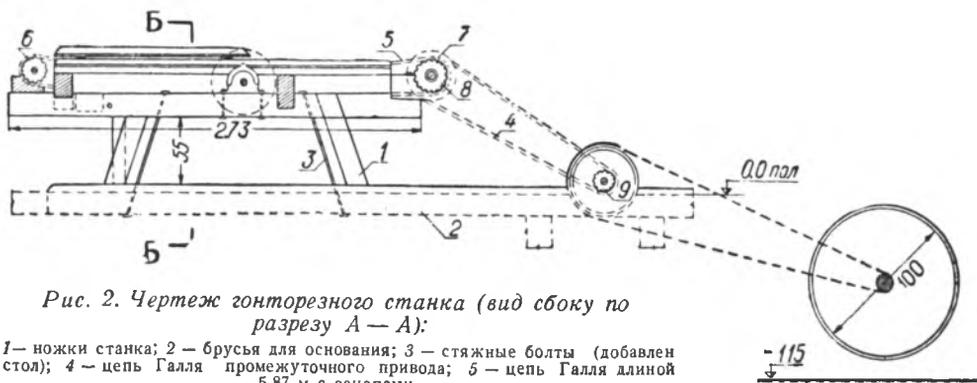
Чертеж гонторезного станка (вид сбоку по разрезу А—А):
